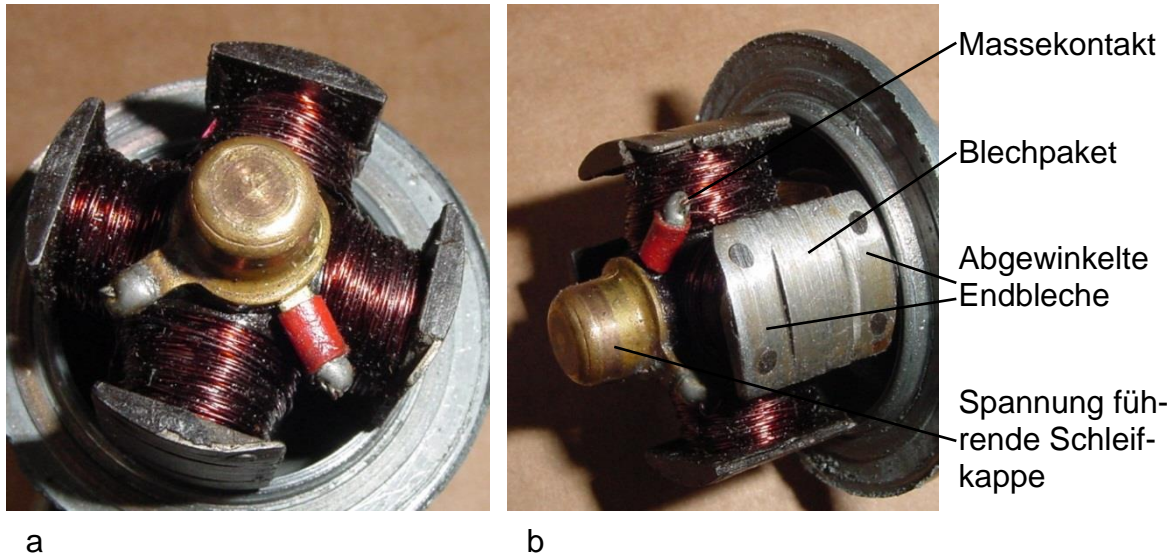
Anker: a) Stirnseite mit der Spannung führenden Kappe, b) Polflächen des Blechpakets (Pollänge: 16 mm, Blechpaketlänge: 6 mm, 10 Bleche 0,6 mm dick, Ankerdurchmesser: 31,5 mm)
